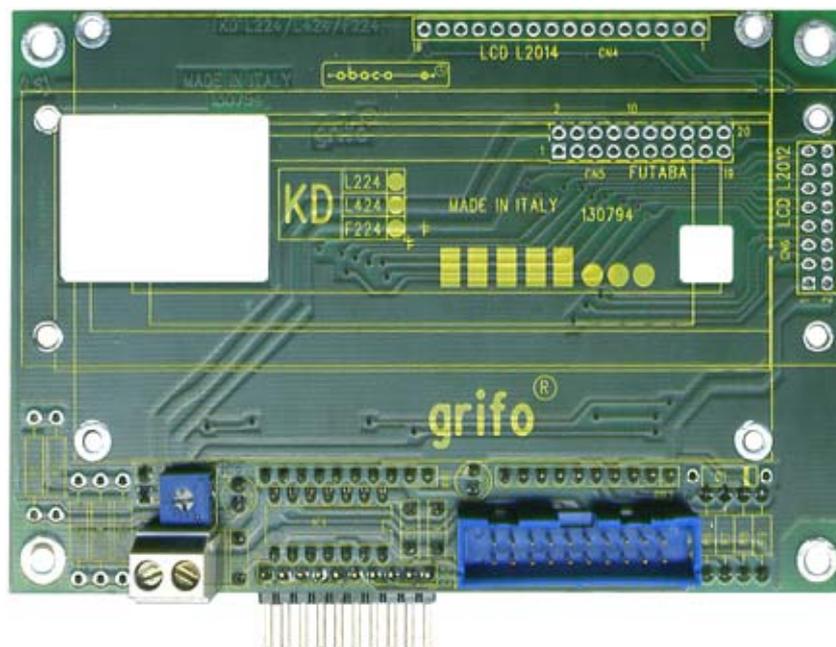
FOTO DELLA KDX-000, LATO SALDATURE
